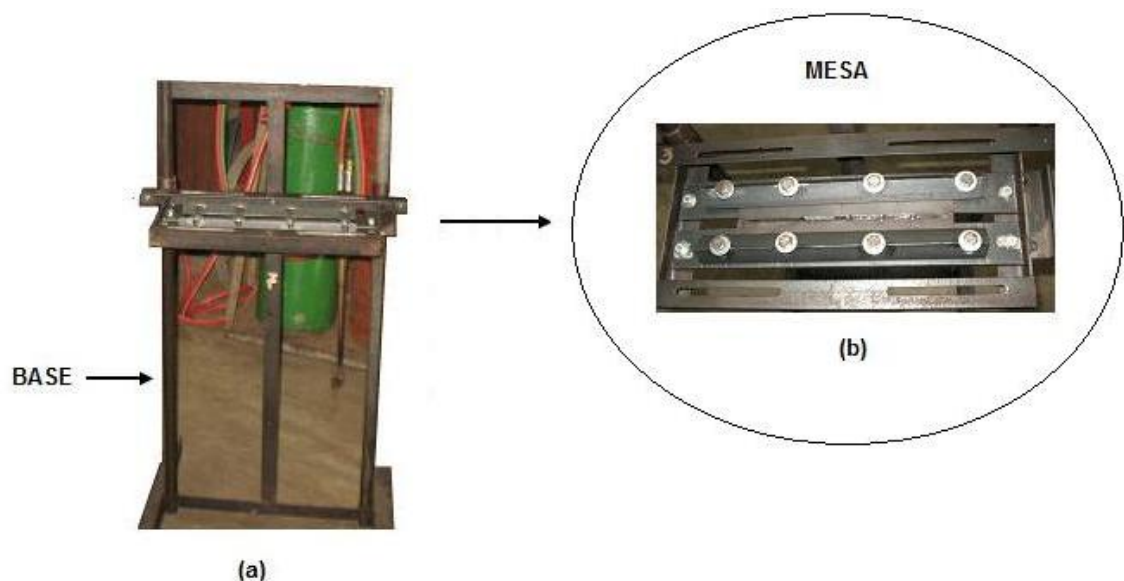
Suporte para soldagem. Base (a) e em detalhe a mesa (b).
